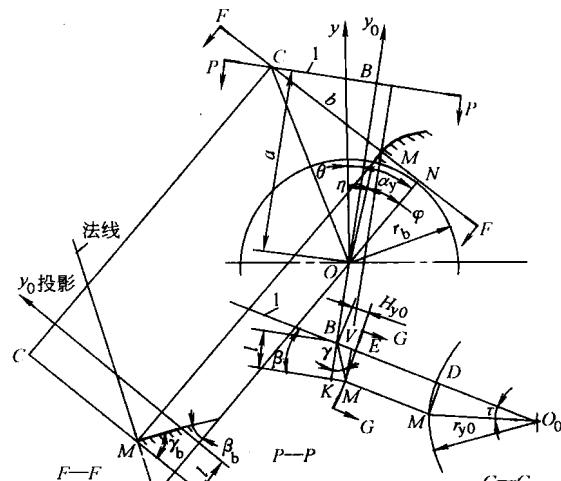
加工斜齿轮时盘形铣刀齿形计算
